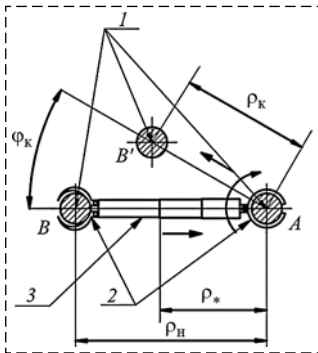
Расчетная схема поворотно-заклинивающего движителя:
